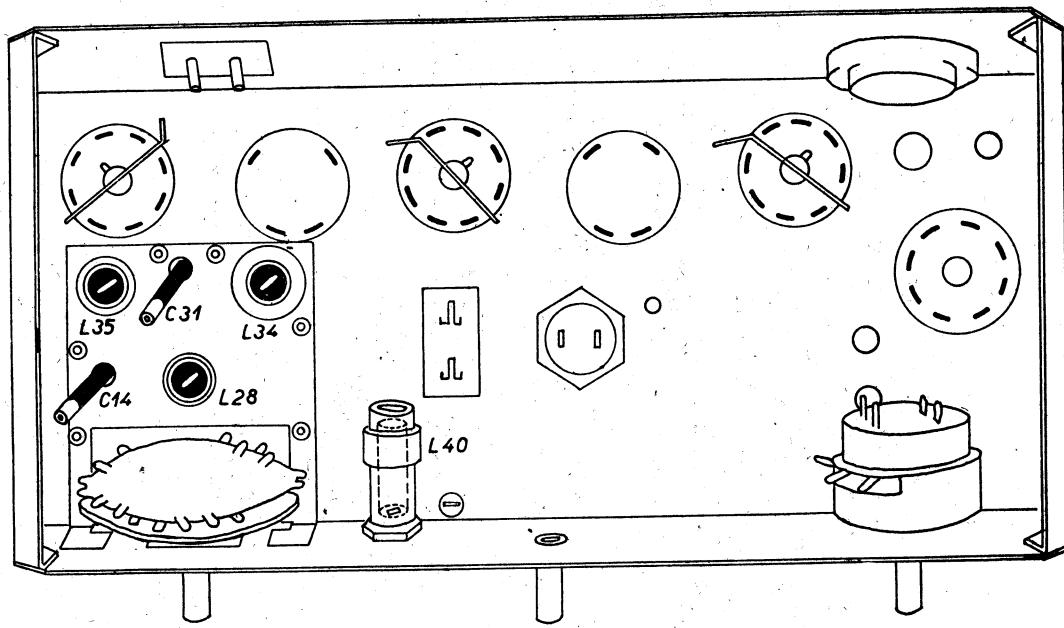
ZAPOJENÍ PŘIJIMAČE NA CHASSIS
